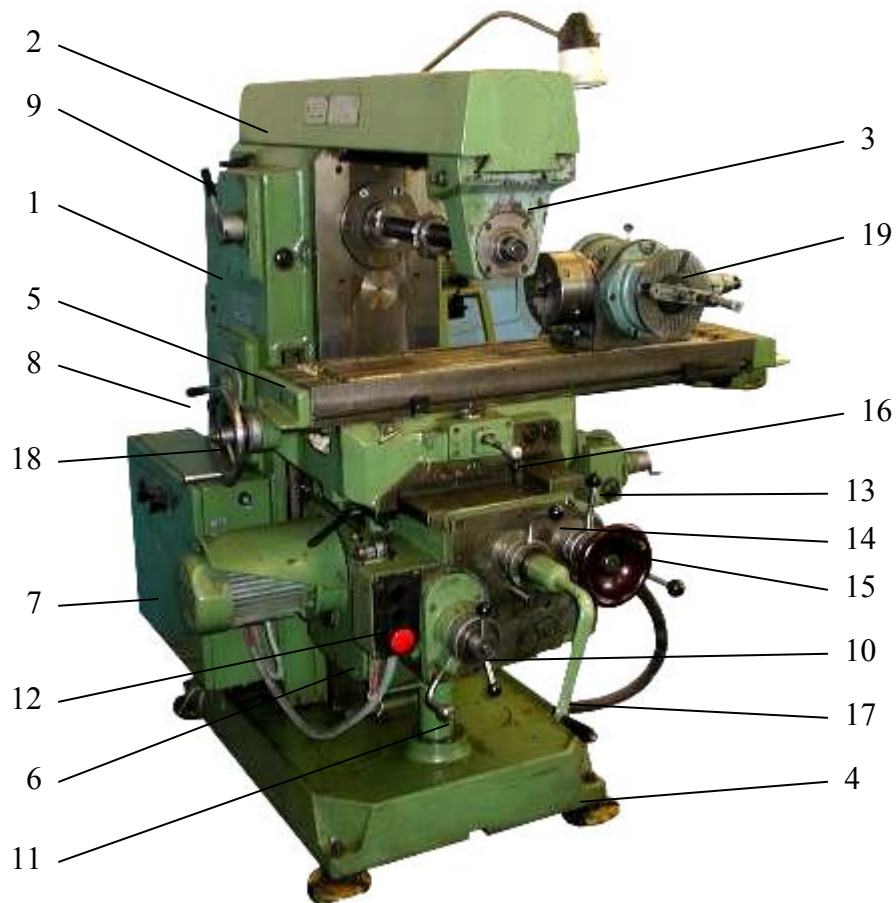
Общий вид универсально-фрезерного станка модели 6P81Г:
